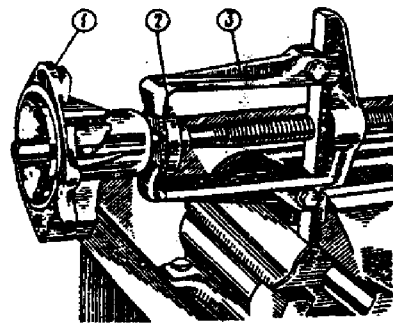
Desmontagem do cubo da polia: 1 - tampa do corpo da bomba; 2 - cubo da polia; 3 - extrator.
